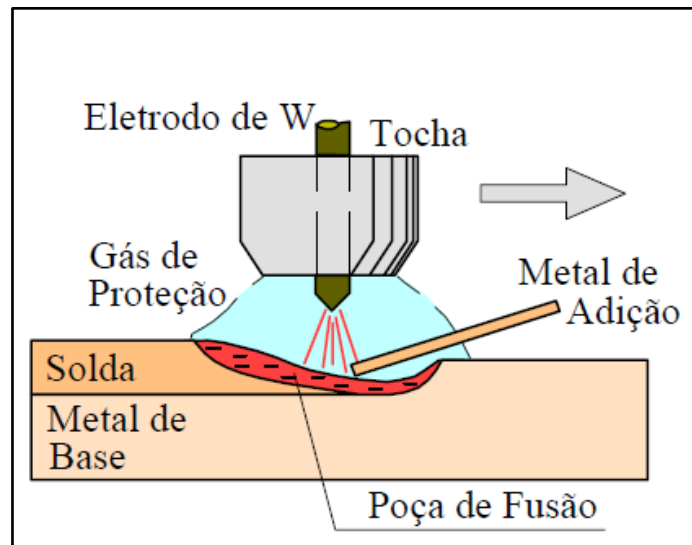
Processo de soldadura TIG [9].
